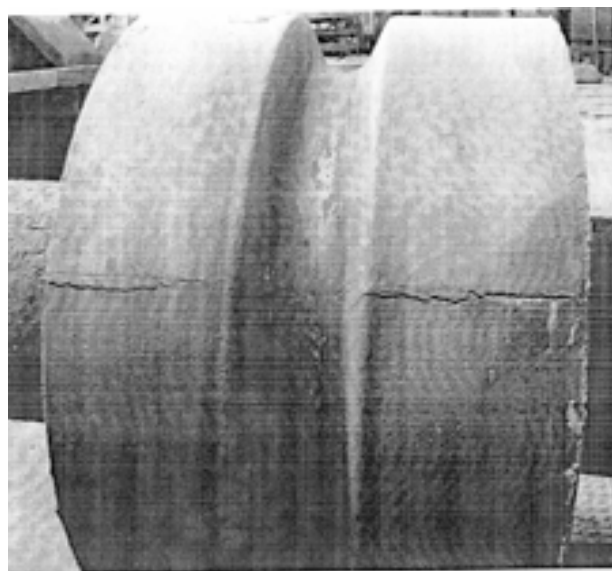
Поздовжня гаряча тріщина на робочому шарі бочки трубопрокатного валка з литим калібром
